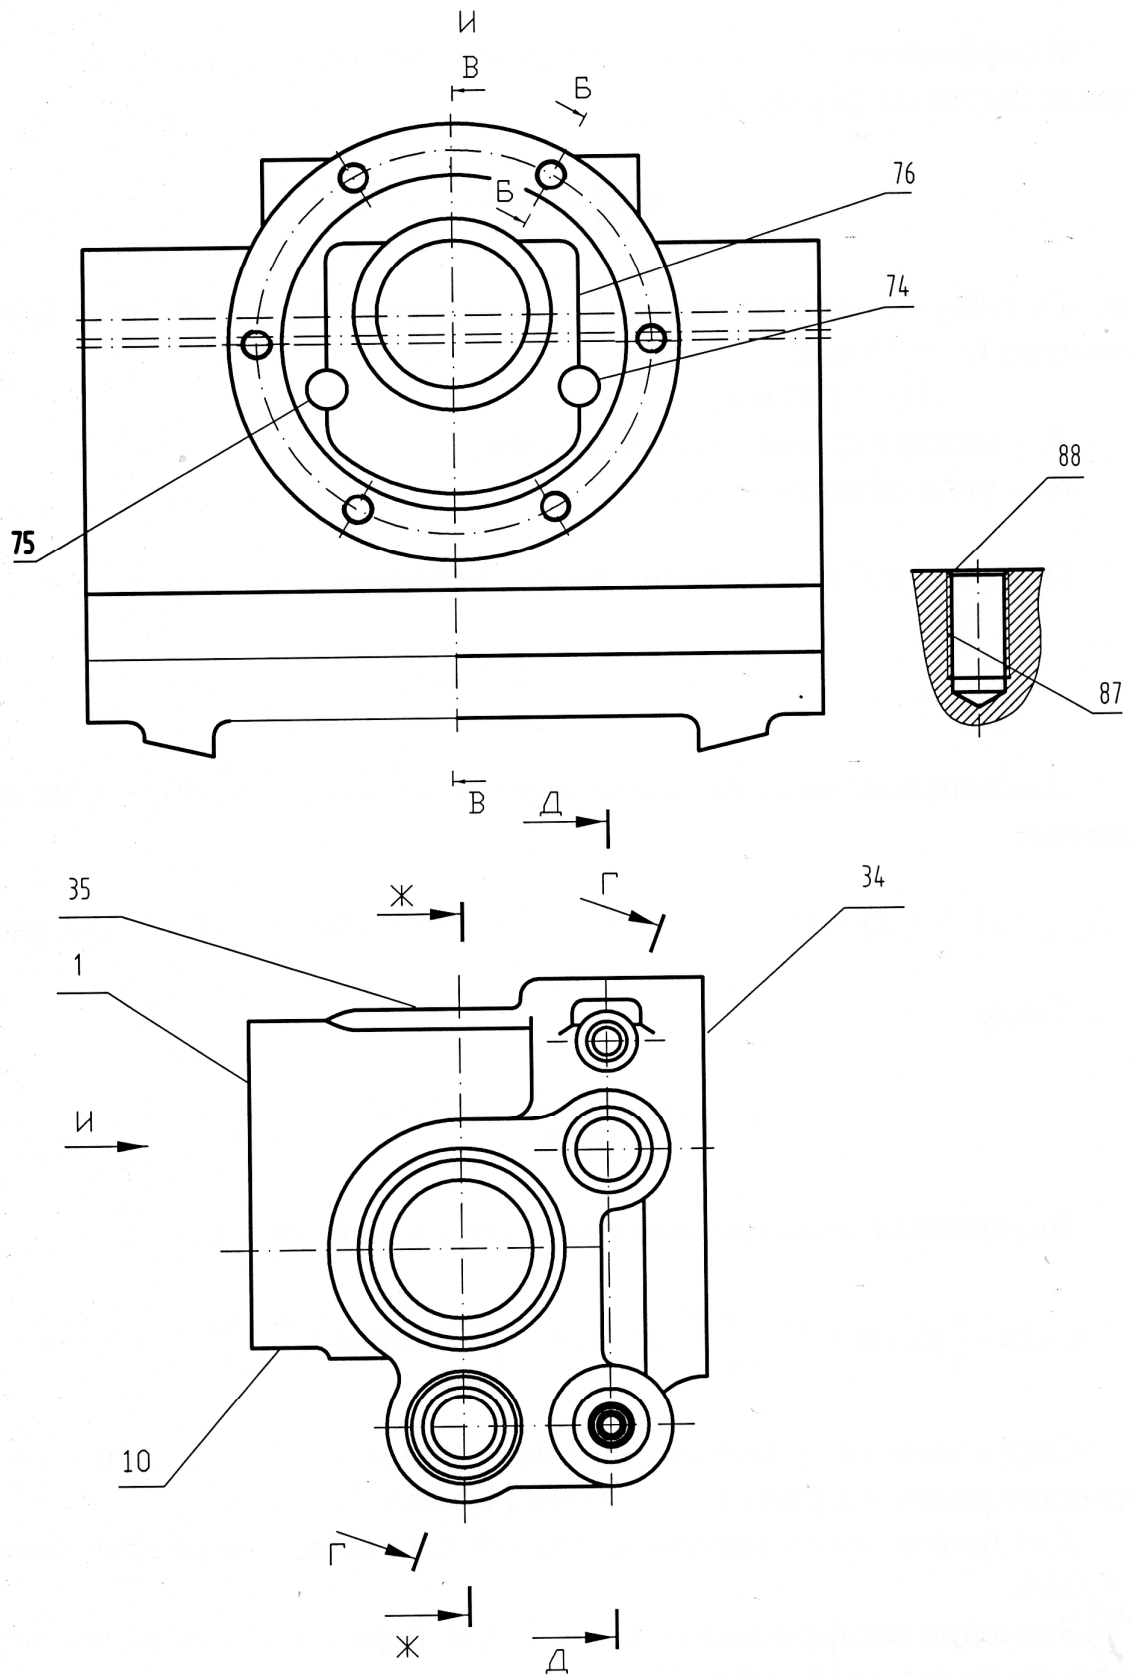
Нумерація поверхнею деталі (Лист 1)
